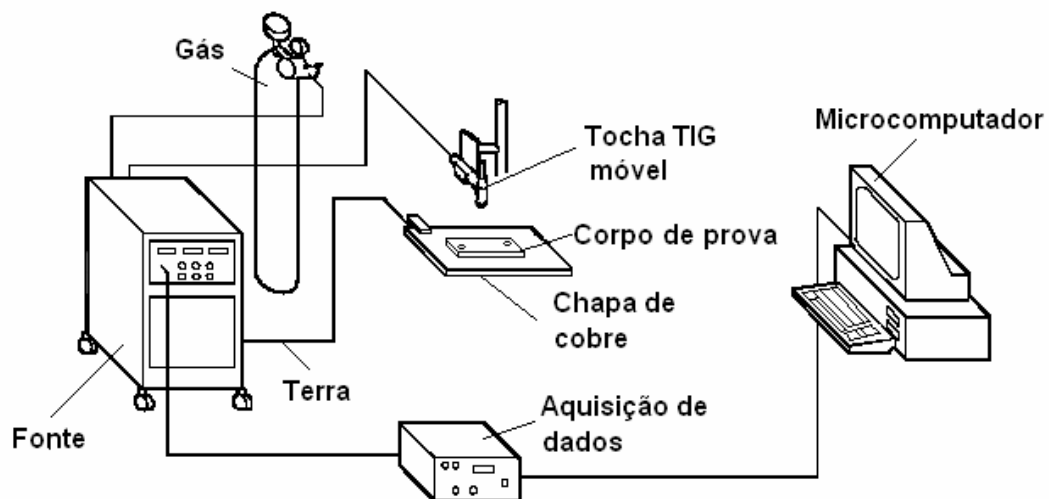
Disposição dos equipamentos de soldagem e aquisição de dados (esquemático).
